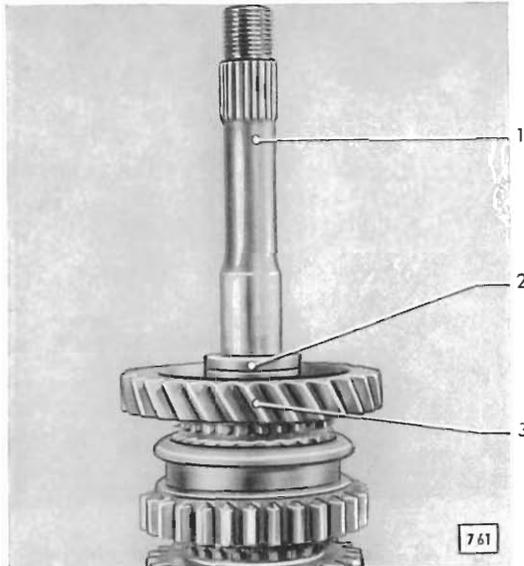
1. Gang-Zahnrad auf Hauptwelle aufgeschoben
